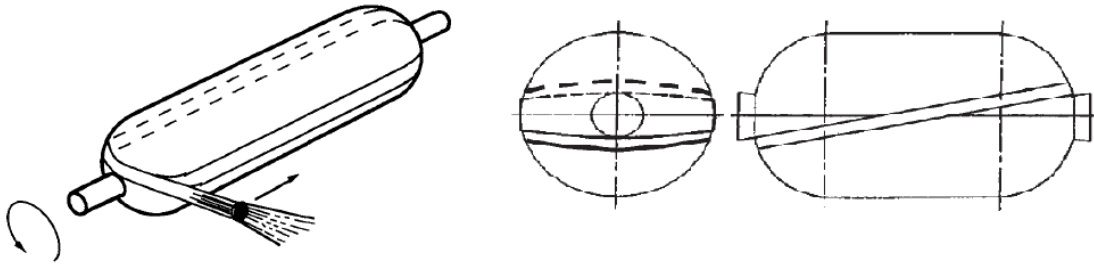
Enrolamento Polar (figura adaptada de [2] e [3])
